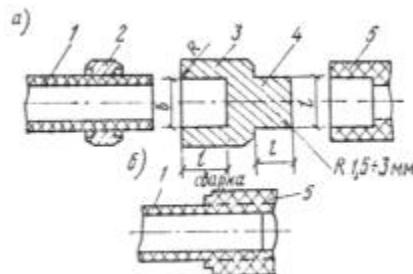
Приспособление для контактной раструбной сварки полиэтиленовых труб и фасонных частей
